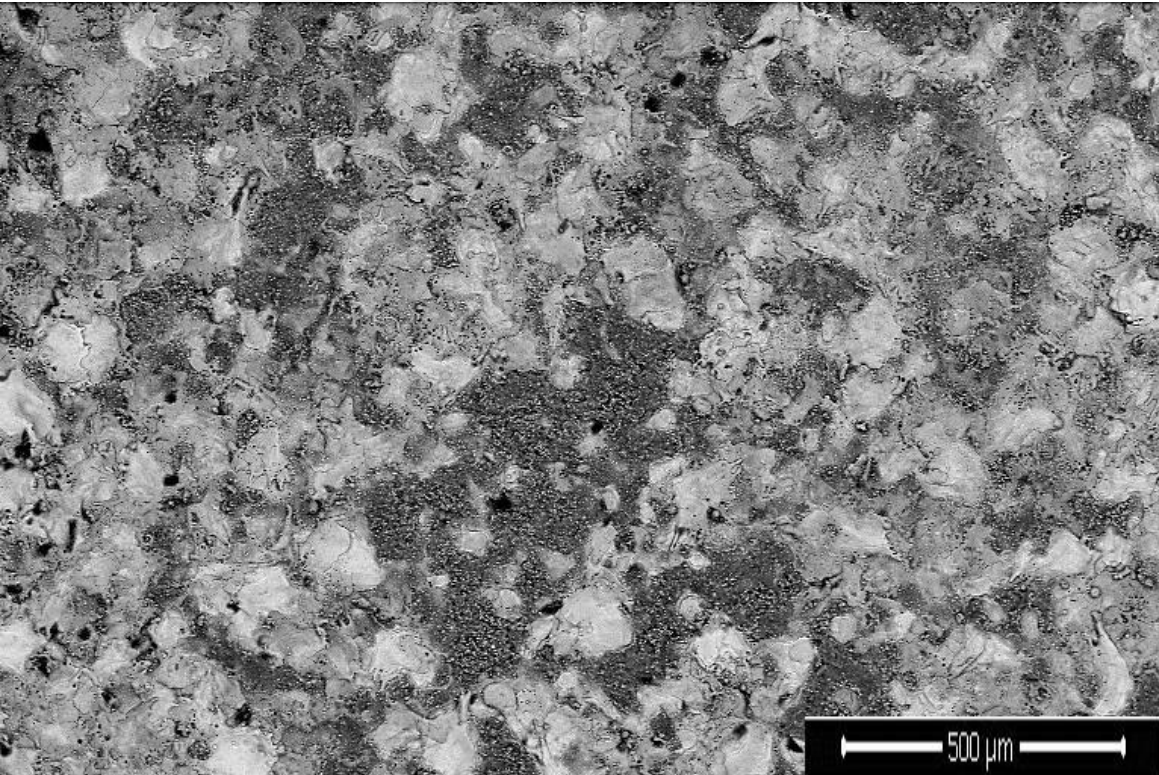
HA-TKEKİ'ye maruz yüzeylerde bir bölgede yoğunlaşan HA tozları (7A, 1600 µs).
